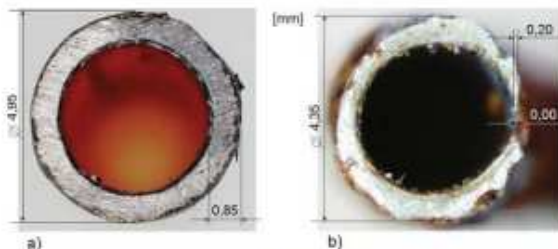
Tloušťka stěny a vnější průměr brzdového potrubí
